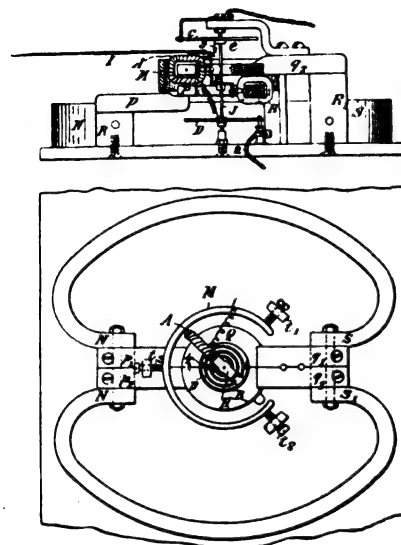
et 7. — Galvanomètre ShalleMBERGER, coupe et plan.
